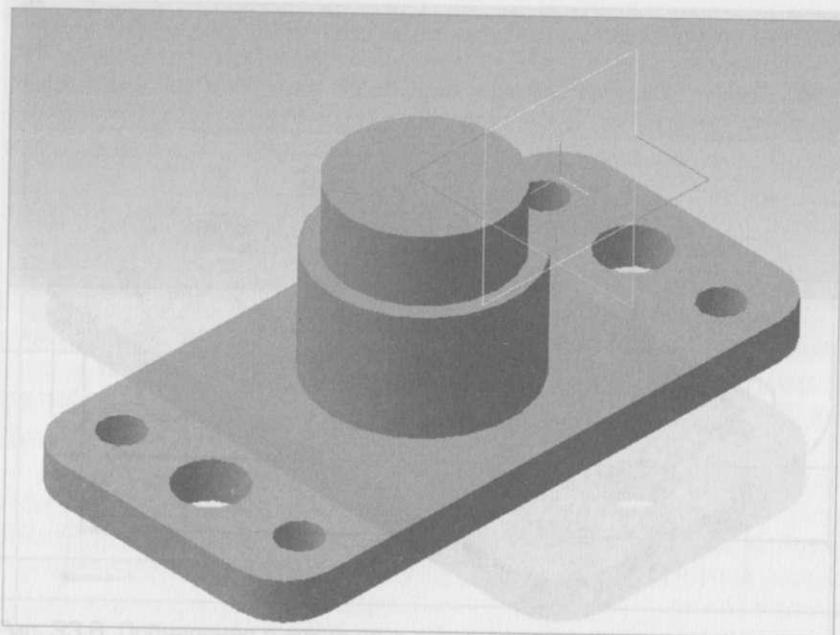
Объемная деталь пластины с двумя цилиндрами
